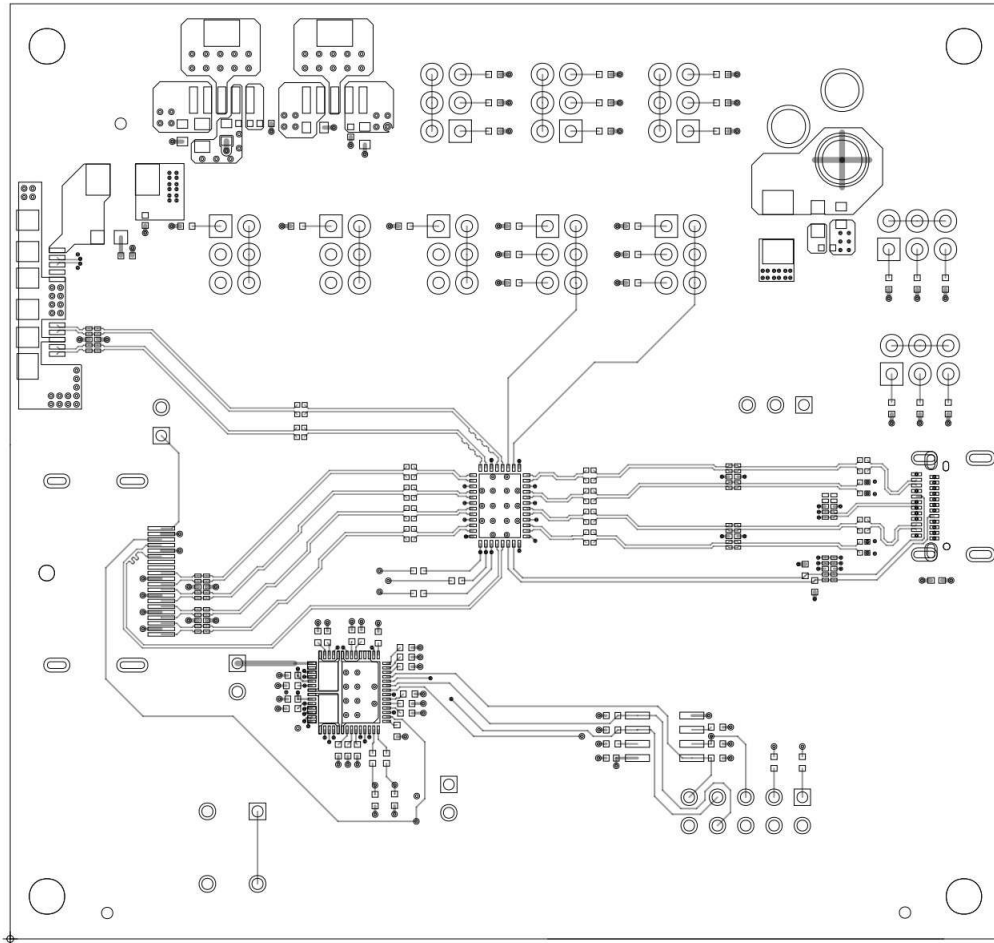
TUSB5461-Q1 EVM PCB 第 1 层 (顶部)
